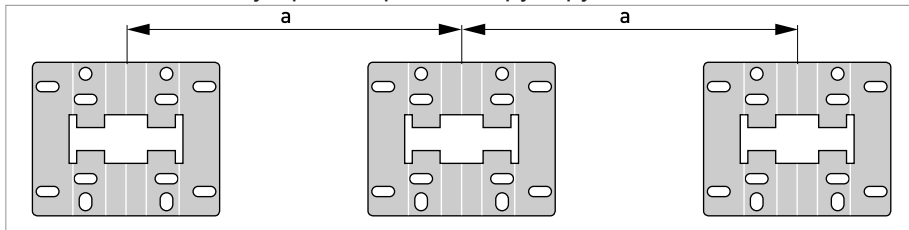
Крепление корпуса конвертера для настенного монтажа
